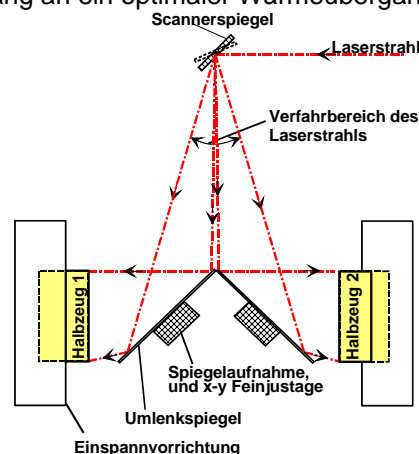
Verfahrensablauf Laserstumpfschweißen
